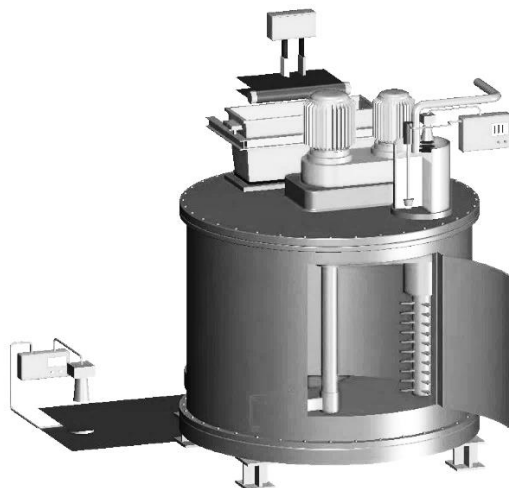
Высокоскоростной турбинный смеситель для приготовления формовочных смесей «УСТ-0701»
